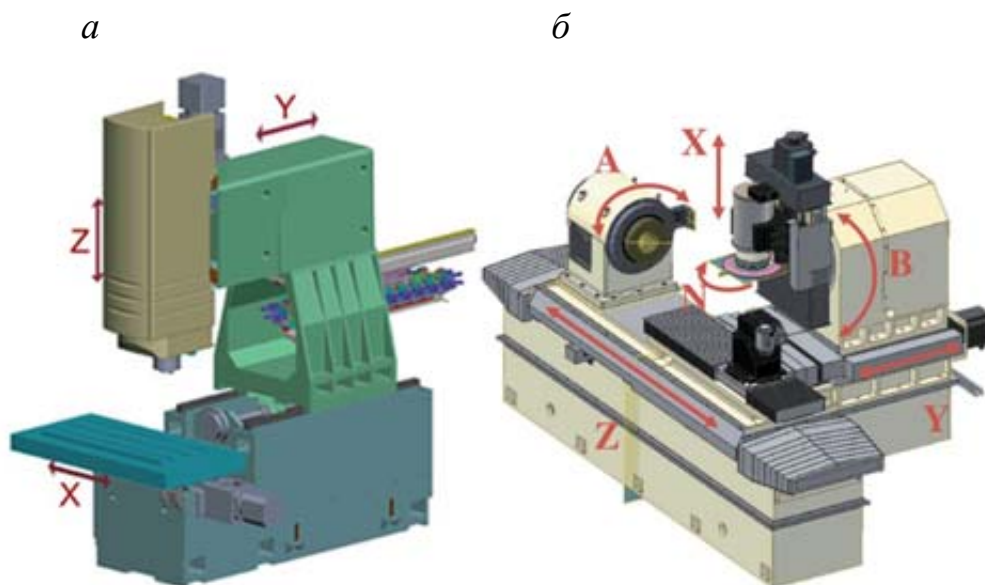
Расположение осей у фрезерных станков с ЧПУ:
